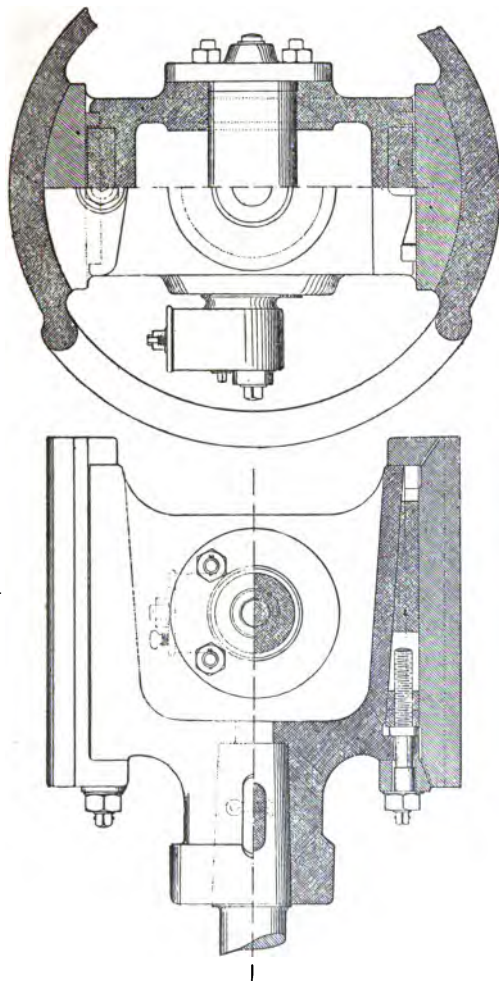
Tête de piston, avec rattrapage de jeu à coin. Coupe longitudinale et élévation ; coupe transversale, montrant les glissières.
